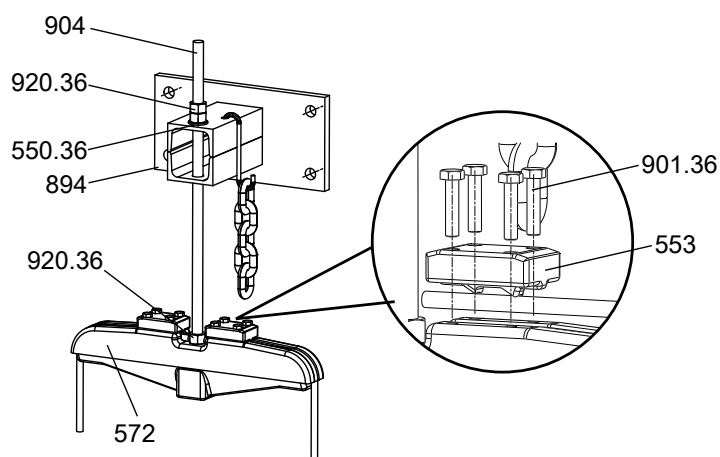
Исполнение консоли для типоразмеров 200-502, 200-503, а также типоразмеров с номинальным диаметром напорного патрубка DN 250 и DN 300
